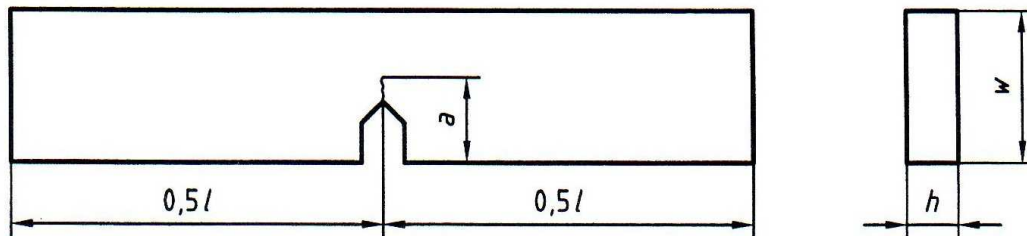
Dimensiones de la probeta del ensayo de fractura.
